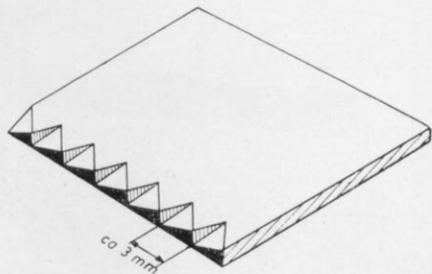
Ziehbrettchen für waagerechte Dachstufen.
